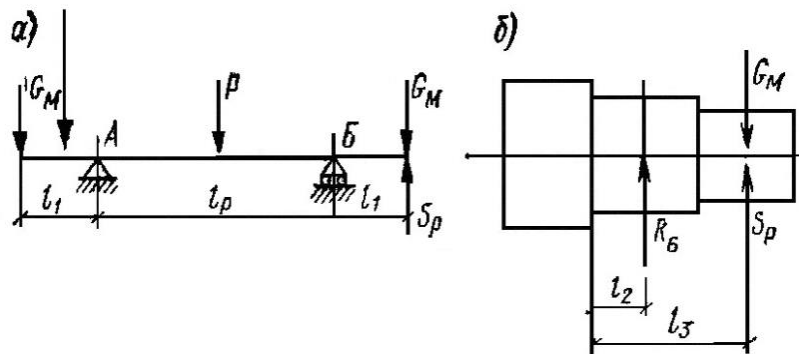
Схемы к определению размеров элементов эксценткового вала: а – диаметр вала; б – диаметр шейки под подшипник
